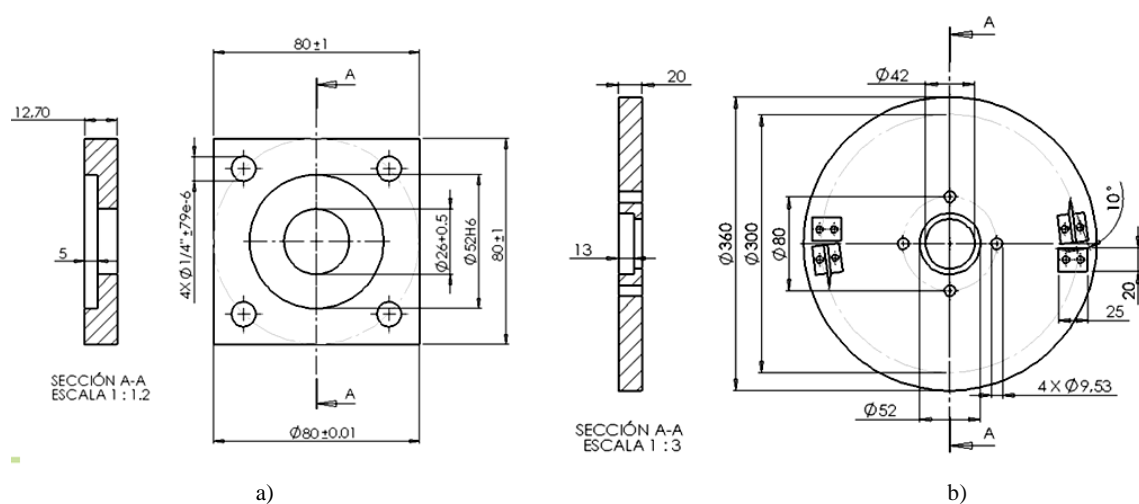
Dimensiones generales: a) Tapa rodamiento. b) tapa del tambor.
